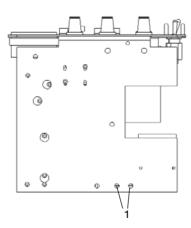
Untere Ansicht auf das Oxylog 1000: Schrauben entfernen
